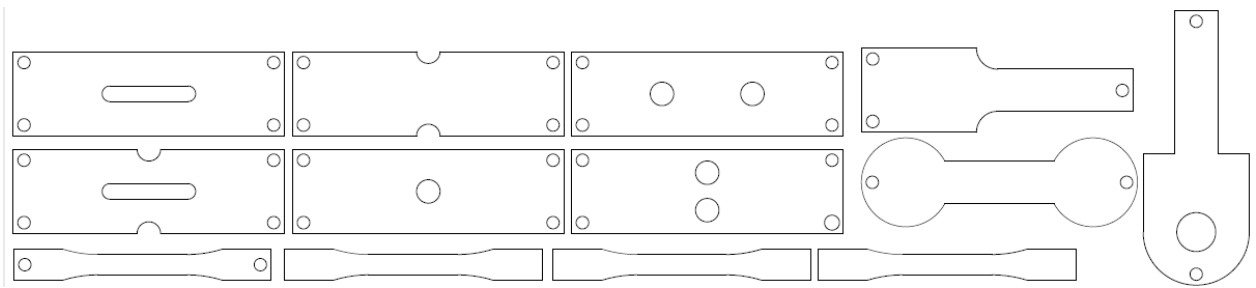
Distribución de las probetas en la primera plancha de resina poliéster.
